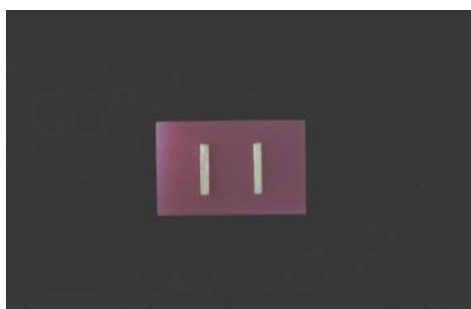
Molde preenchido com o conjunto gesso/lama de alumina
